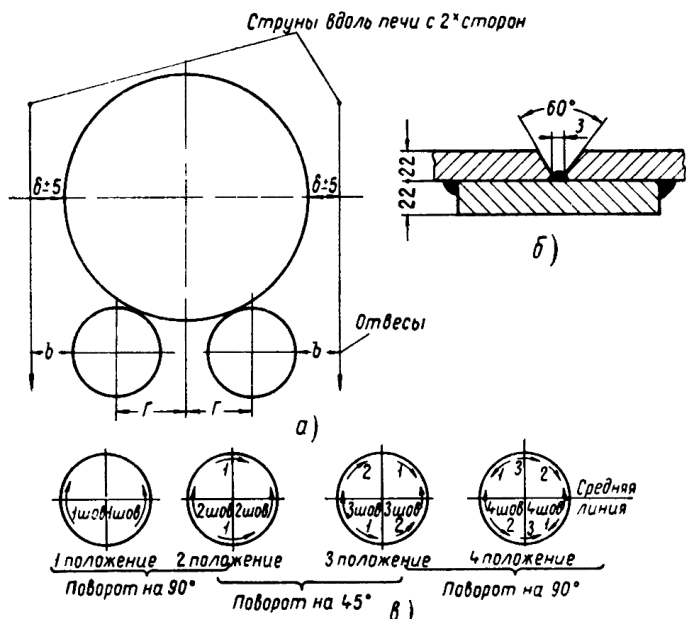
Схема проверки прямолинейности корпуса печи (*а*); окончательная сборка секции с установленной накладкой (*б*); схема последовательности сварки монтажных стыков (*в*)
